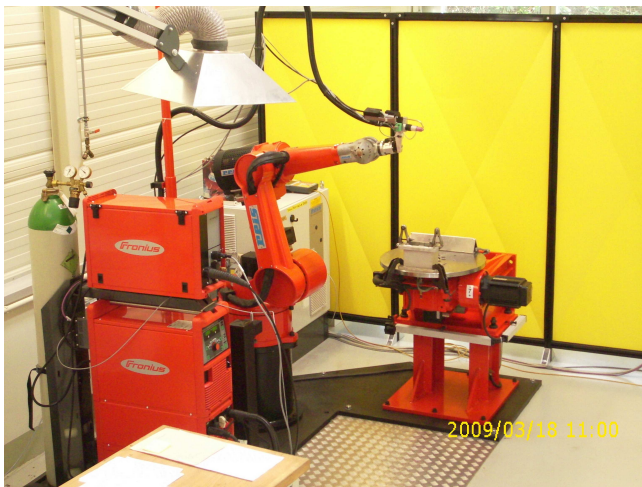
Schweißroboter für Aluminium-Schweißungen.
